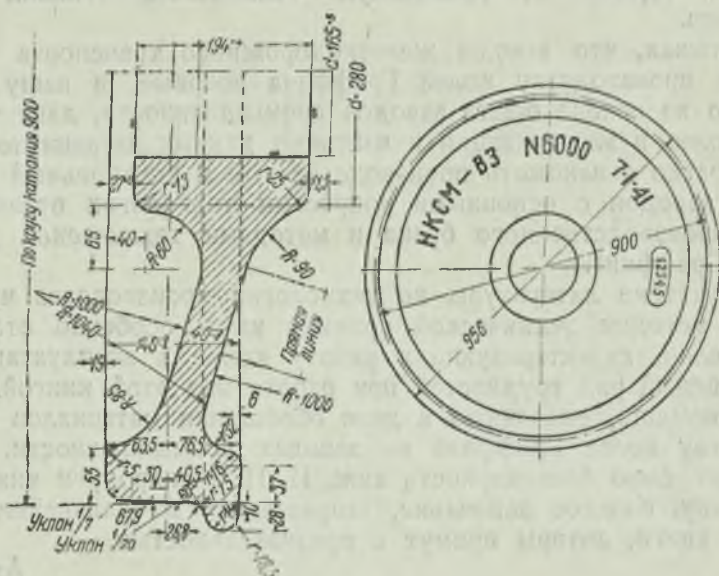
Колесо Гриффина стандартного типа. Профиль катания колеса отливается согласно чертежу ВНИИ НКПС № КС-10—1 от 25/V 1934 г.
